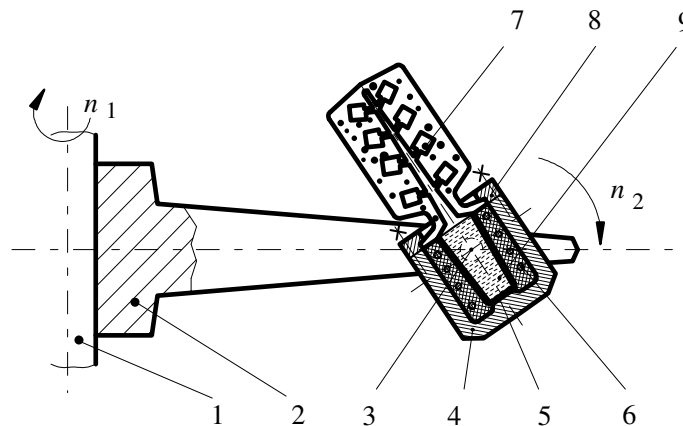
Turnarea centrifugală cu axă de rotație excentrică:
